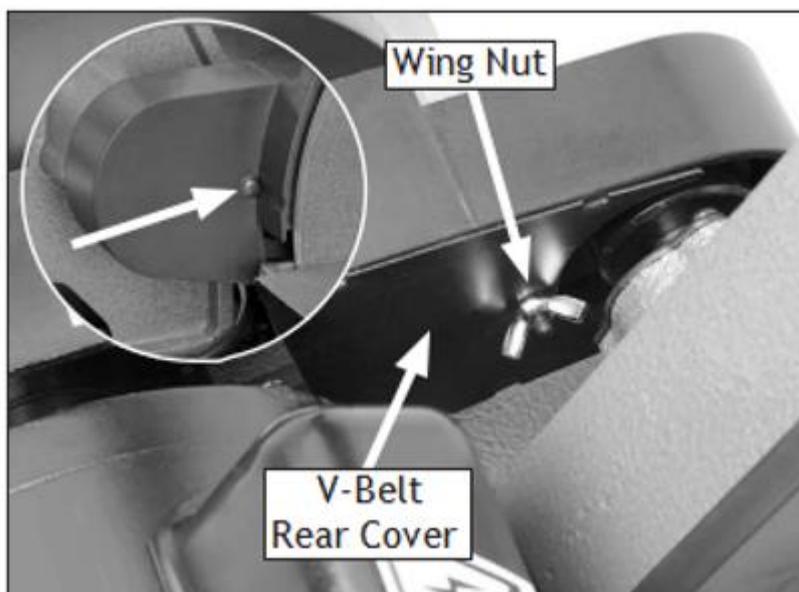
Установлена задняя крышка клинового ремня (на вставке показано расположение винта спереди).
